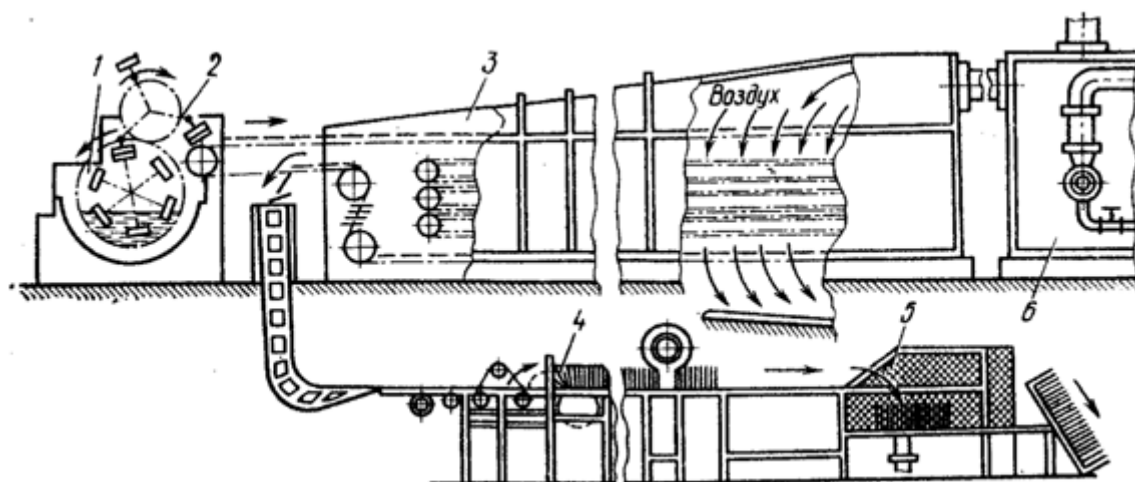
Схема установки для изготовления прокладок из бумажного литья:
